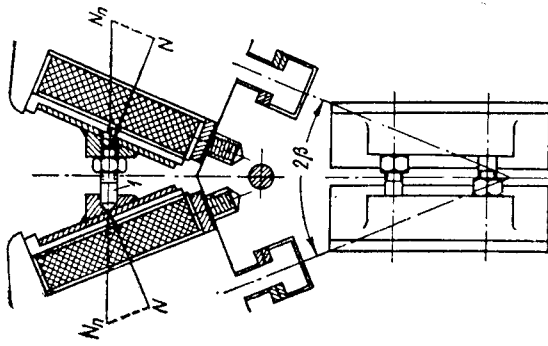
Межполюсная распорка с расклинивающими винтовыми шпильками
